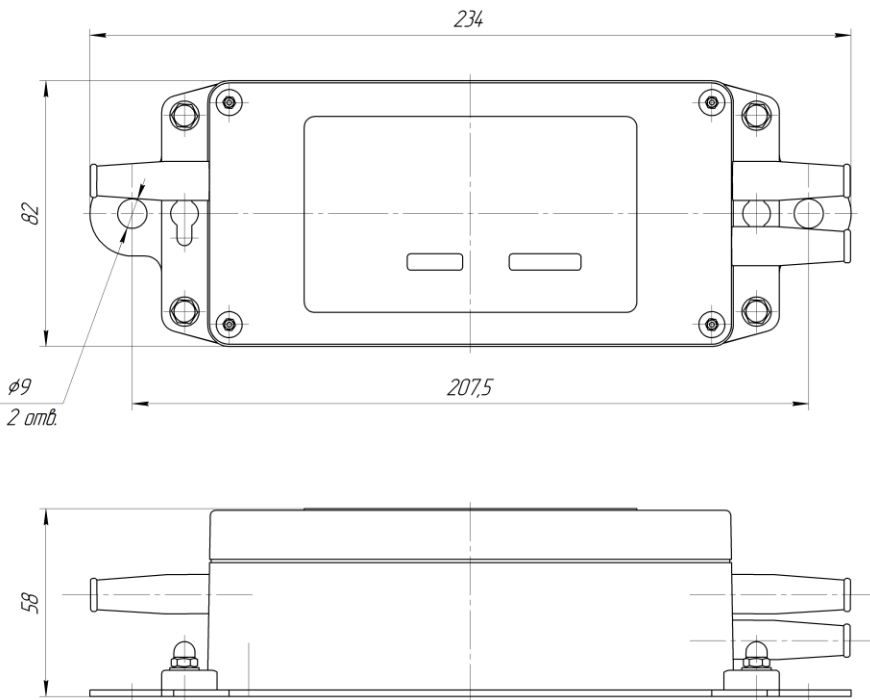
Габаритные и установочные размеры устройство зарядное 220В
